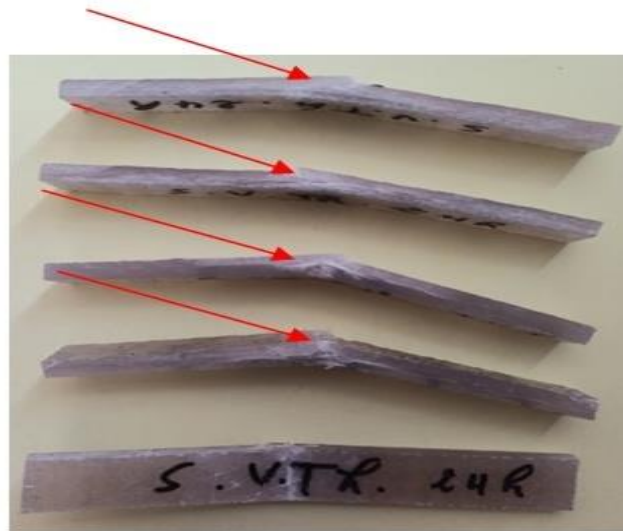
Rupture des éprouvettes du tricouches vieilli 24h
